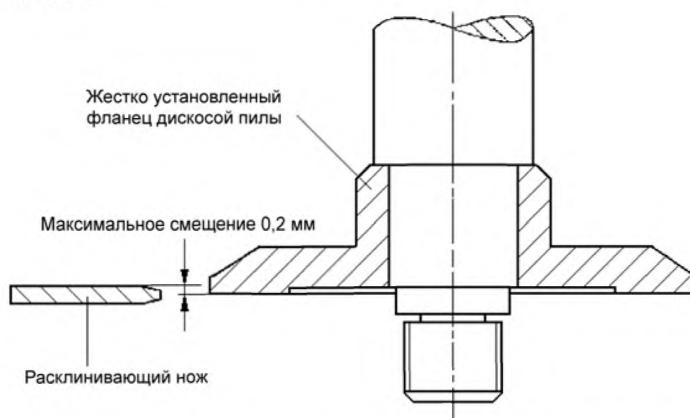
Установка расклинивающего ножа относительно жестко установленного фланца дисковой пилы
